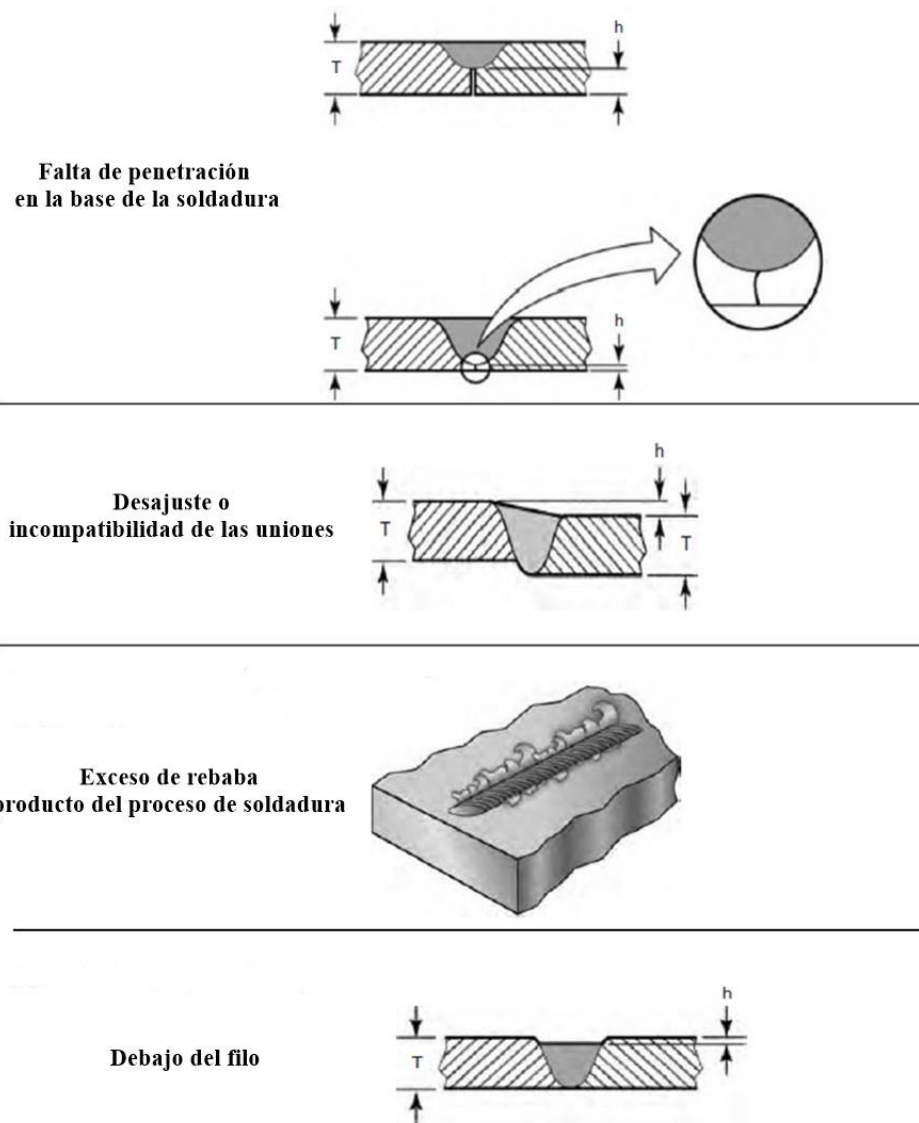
Tipos de discontinuidades de soldadura producidas por FSW (44)
